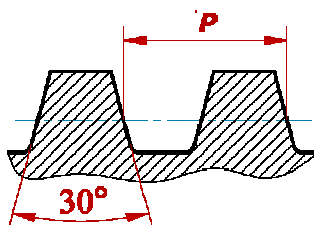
Вид трапецеидальной резьбы : Р - шаг резьбы; 30° - угол профиля резьбы
